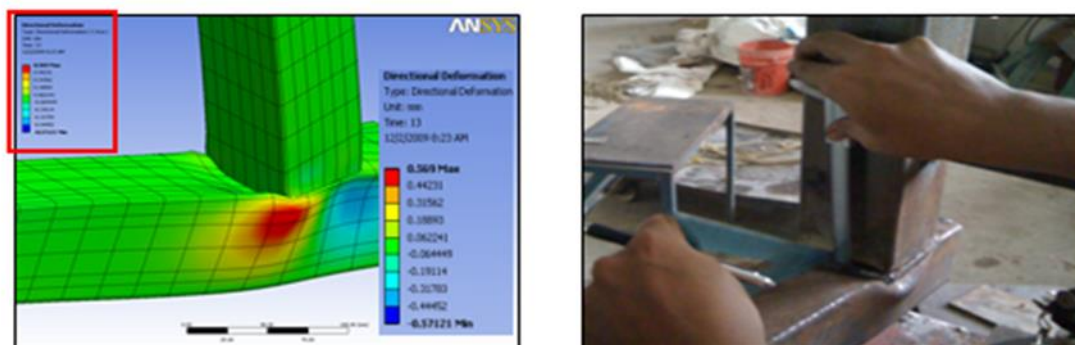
a) Distorsión teórica. 20, b) Distorsión experimental ensanchamiento de la sección transversal de la columna del pórtico parámetro llamado (b_1) tubos de 70x70x2.25mm. Ensayo 2. Fuente: [8]
